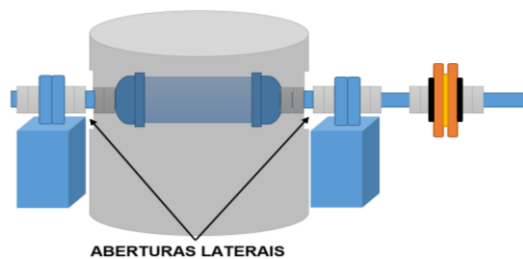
Eixo colocado por dentro das aberturas laterais da coluna de apoio.
